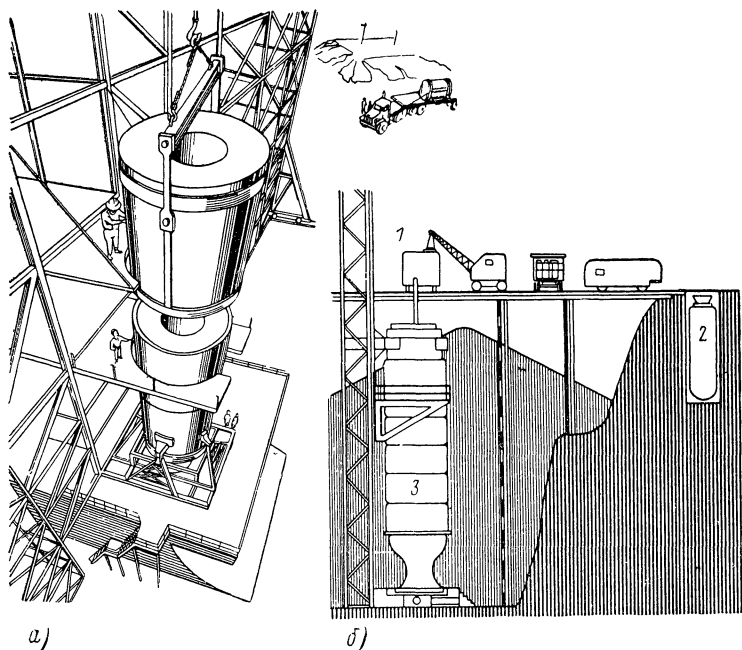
Мощные ракетные двигатели твердого топлива могут изготавливаться двумя методами:
